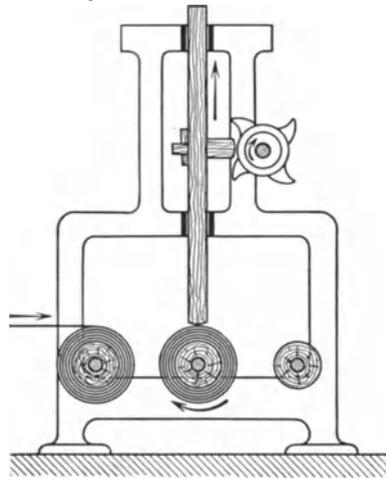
Querschnitt eines Stampfkalanders. (Aus Kozlik: Technologie der Gewebeanfertigung S.215. Berlin: Julius Springer 1908.)
